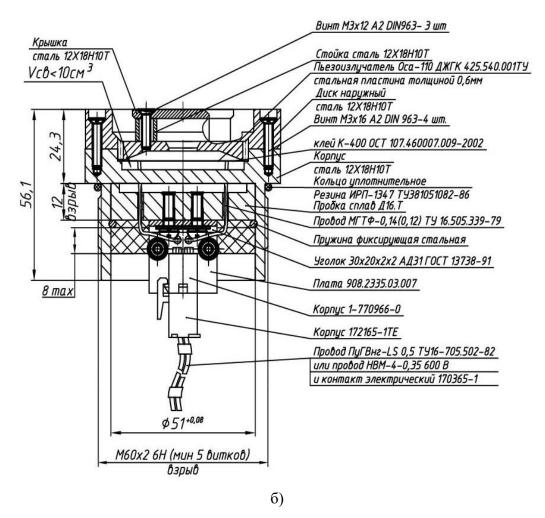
Варианты конструкции пьезоизлучателя для табло в нержавеющем корпусе. На рис. 4.6 применён разъём (корпус 172165-1TE) для удобного отделения проводов пьезоизлучателя от крышки при её снятии
